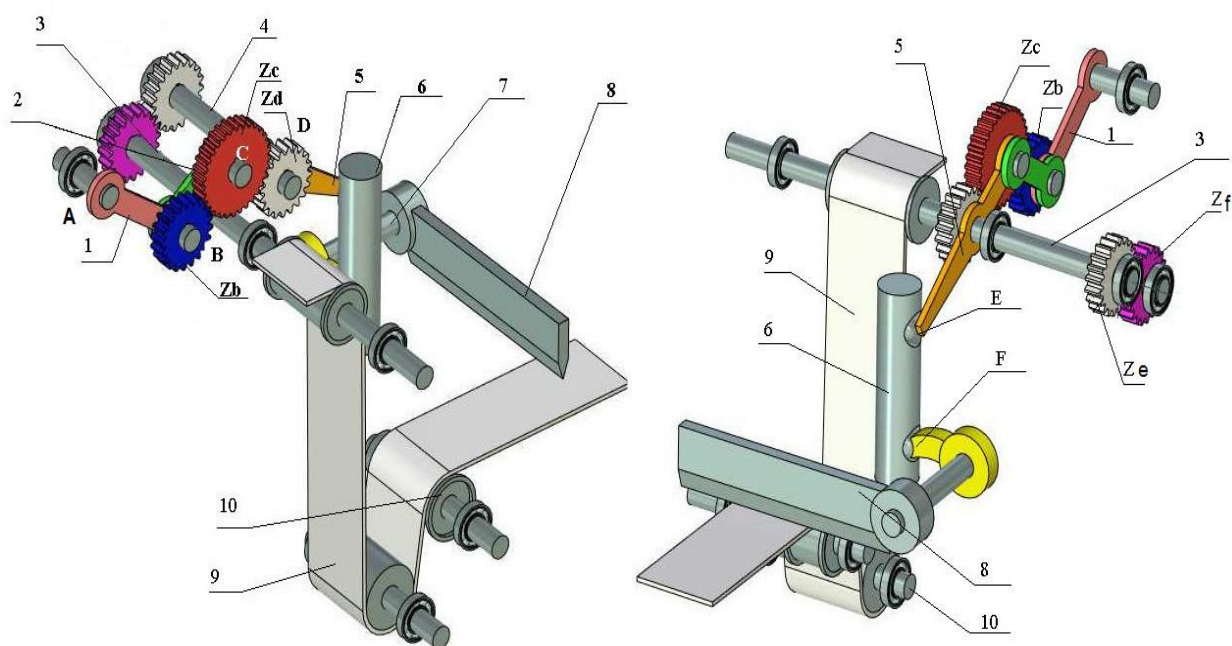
Схема устройства механизма подачи бумажной ленты упаковочного автомата
